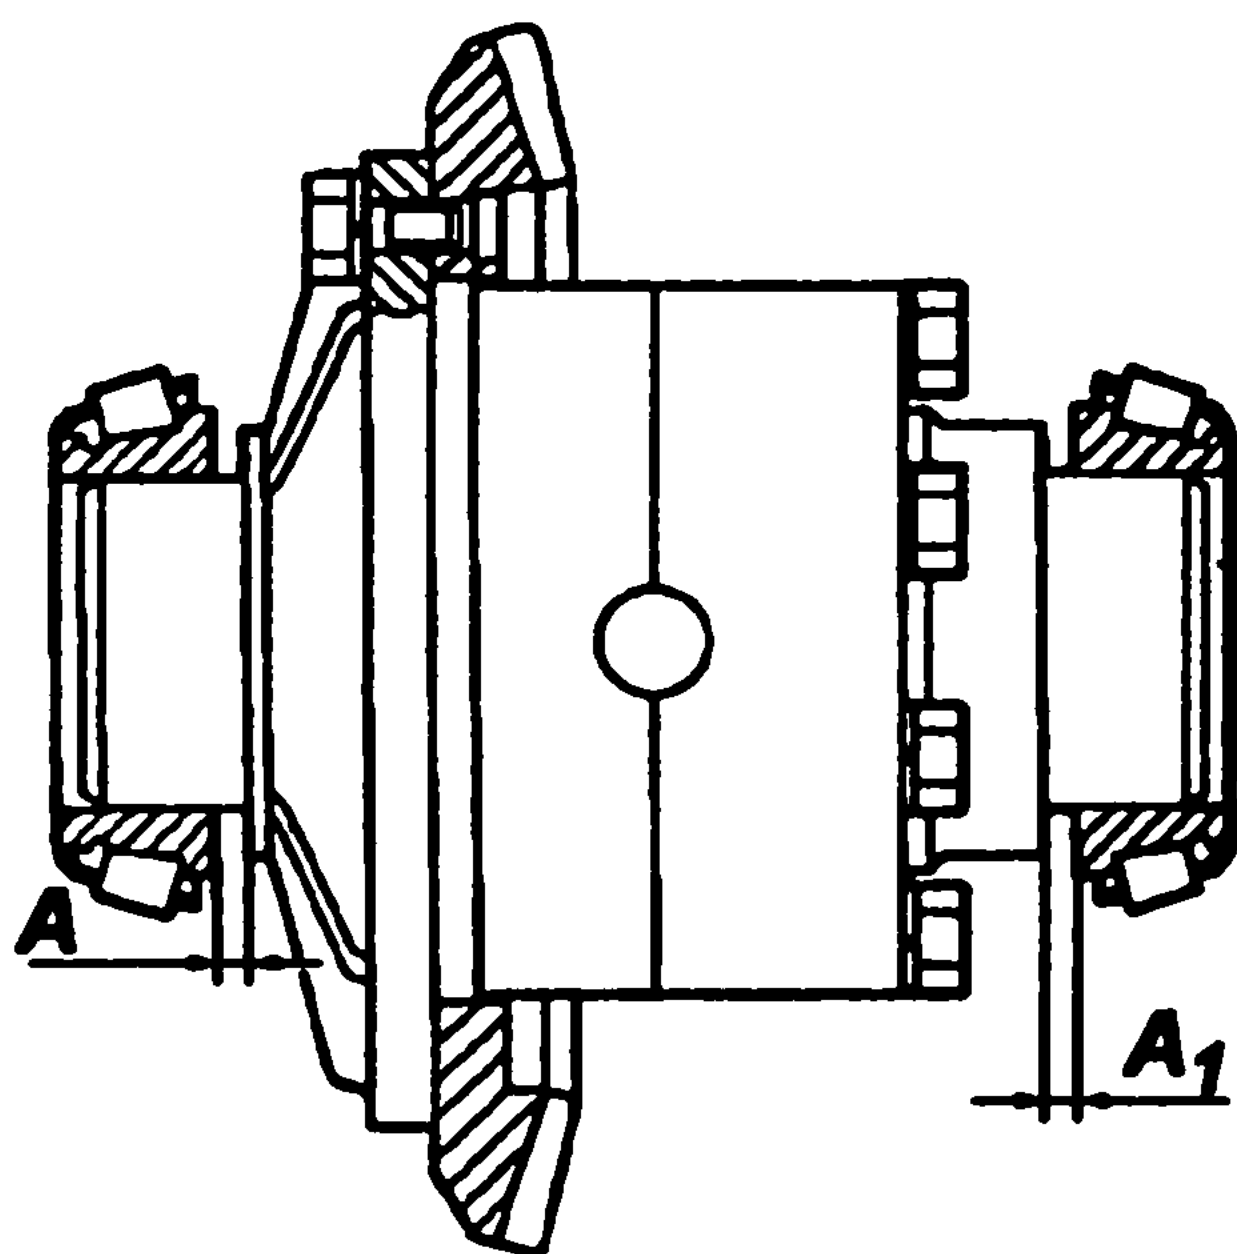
Зазоры A и A_1 между торцами подшипников и коробки сателлитов
